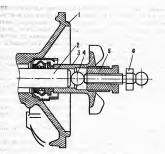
Съеминк крыльчатки из деталей собственного мотора: 1 — крышка водяного насоса; 2 — валик; 3 — крыльчатка; 4 — шарик; 5 — втулка регулирования клапана; 6 — регулировочный болт.
